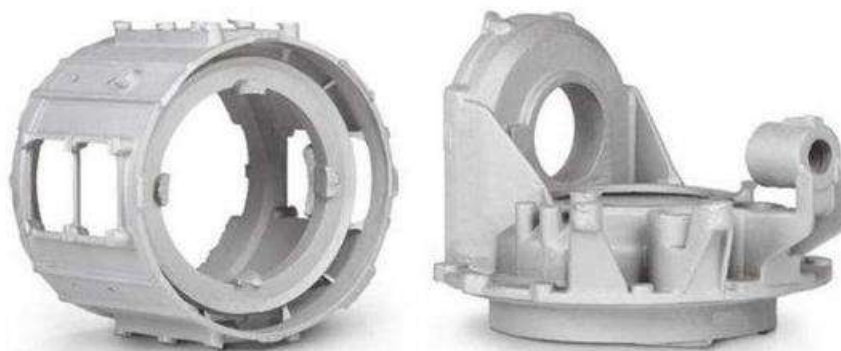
Корпусні виливки, виготовлені з титанового сплаву VT5L, для авіаційної промисловості.
